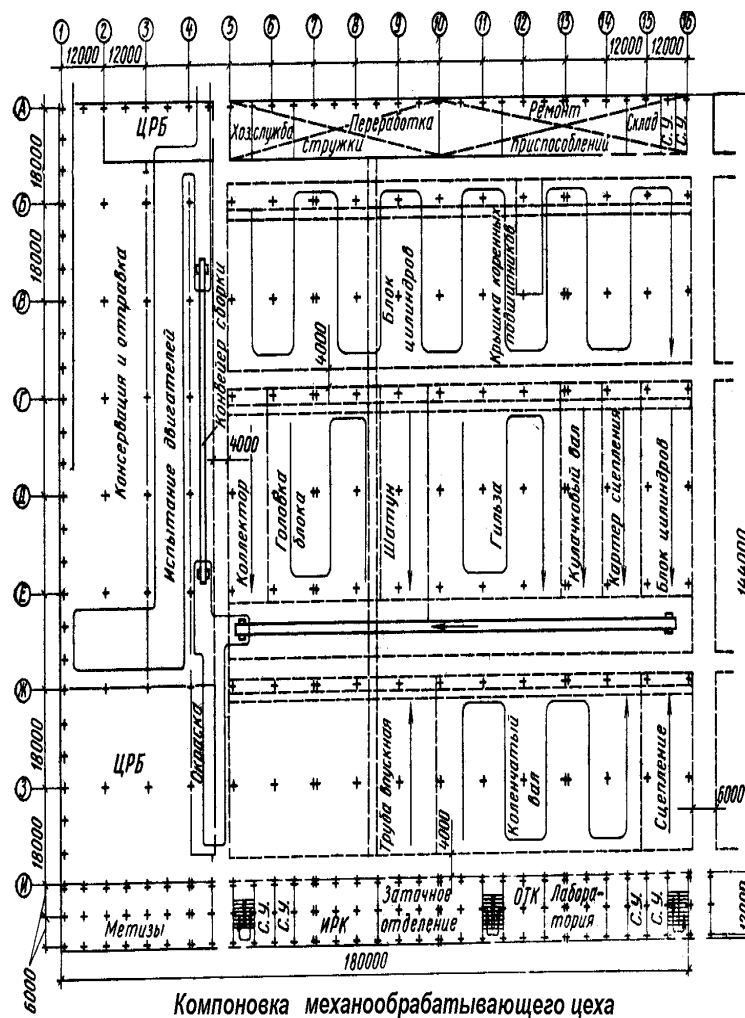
Компоновка механообрабатывающего цеха
